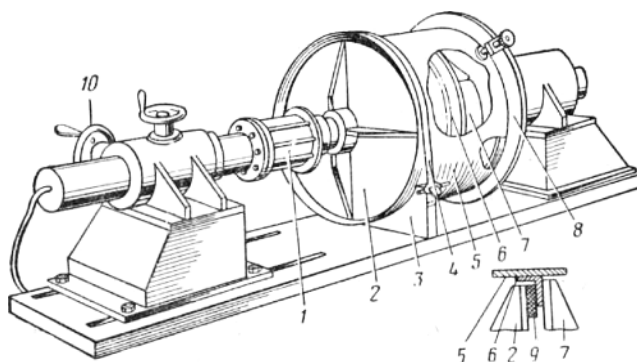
Стапель для сборки обечаяк со шпангоутами: 1 – пневмоцилиндр, 2 – подвижная плита-планшайба, 3 – ложемент, 4 – гибкая лента; 5 – обечайка; 6 – шпангоут; 7 – упор; 8 – планшайба; 9 – резина; 10 – маховик
